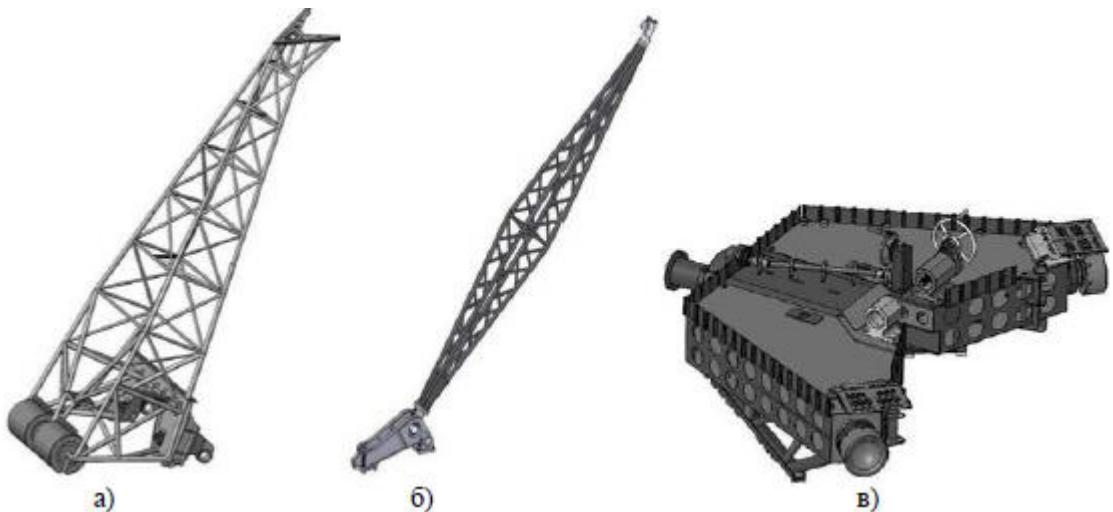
Элементы ферм–опор, где а) опорная ферма с противовесами, б) несущая стрела, в) сектор силового пояса
